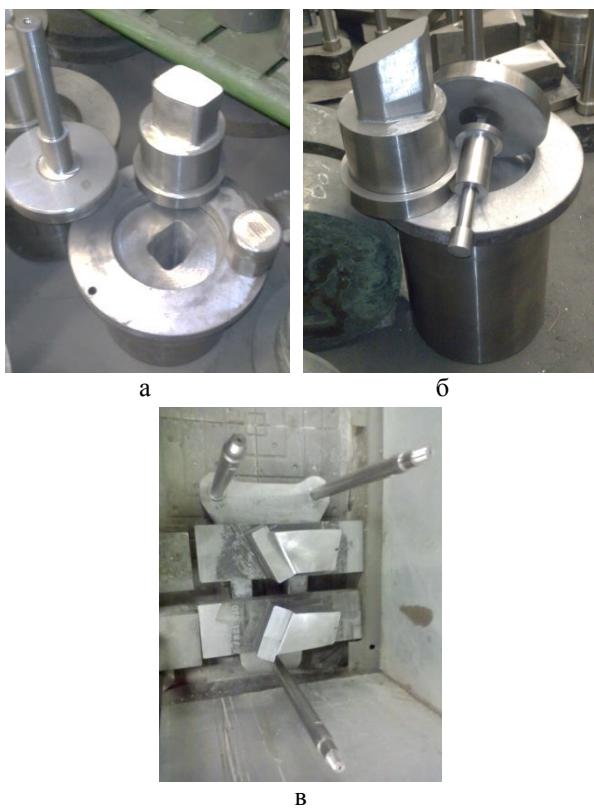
Штампы для изготовления поковки имитатора лопатки: а – для закрытой осадки; б – для прямого выдавливания; в – для закрытой штамповки
